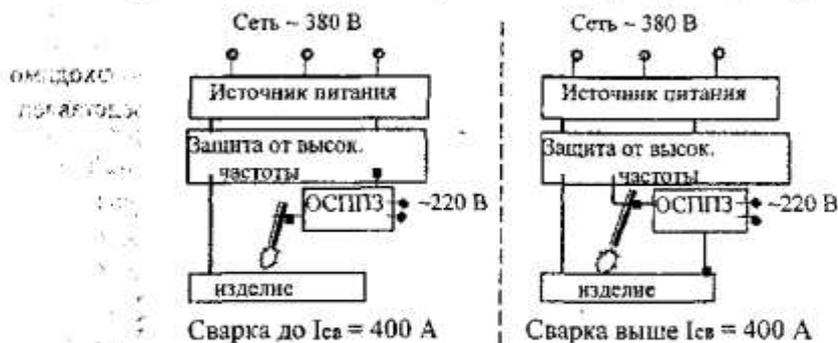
Схема включения осциллятора в сварочную цепь
